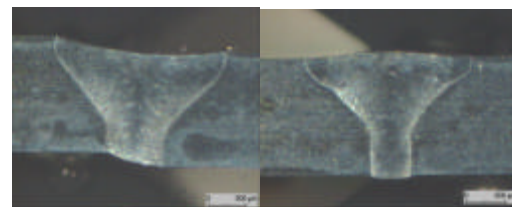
Querschnitte Schweißnähte Stahl 1.4571 bei 1,5 mm Blechdicke und 2,3 kW Laserleistung: links Blindnaht ( $v = 32$  mm/s) und rechts I-Naht ( $v = 36$  mm/s)
